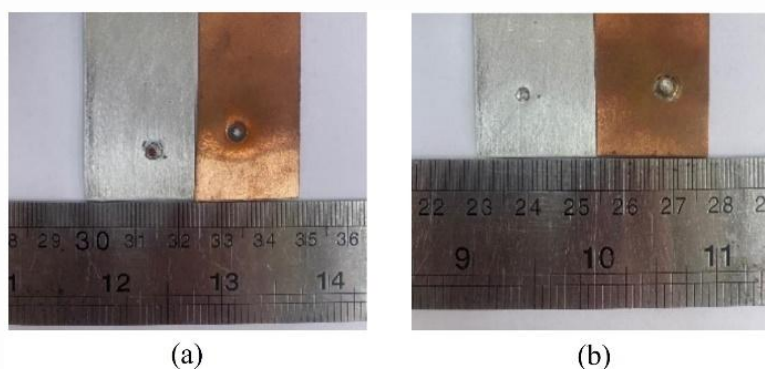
Pengukuran diameter *nugget* spesimen las (a) Konvensional - *Tool 2* (b) *Two stage* - *Tool 2* dan *Tool 4
